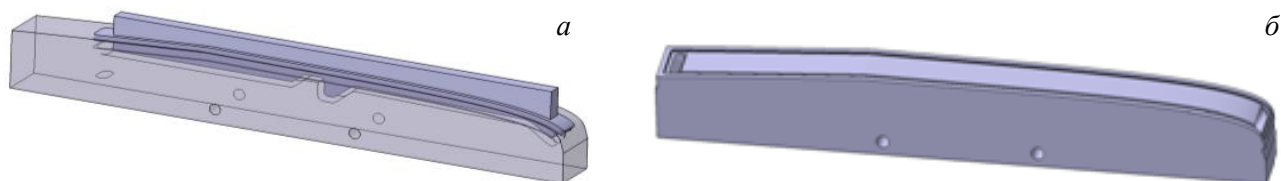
Корпус пальца ППС: *а* — заготовка корпуса пальца под сварку; *б* — корпус пальца после механической обработки
